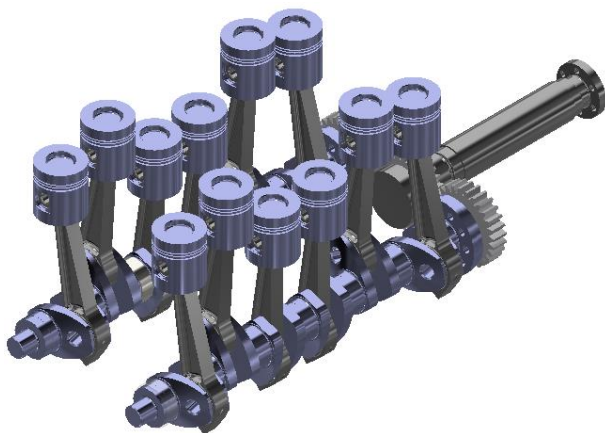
Кривошипно-шатунный механизм двухрядного двухвального поршневого двигателя
